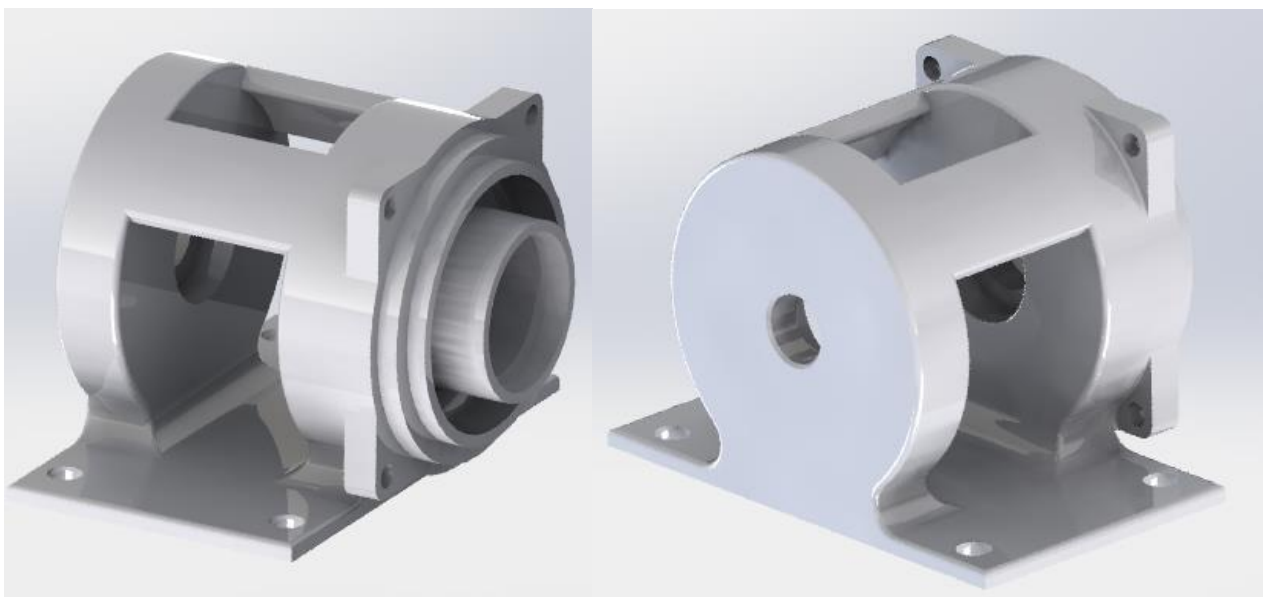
Diseño CAD de la carcasa de la bomba.
